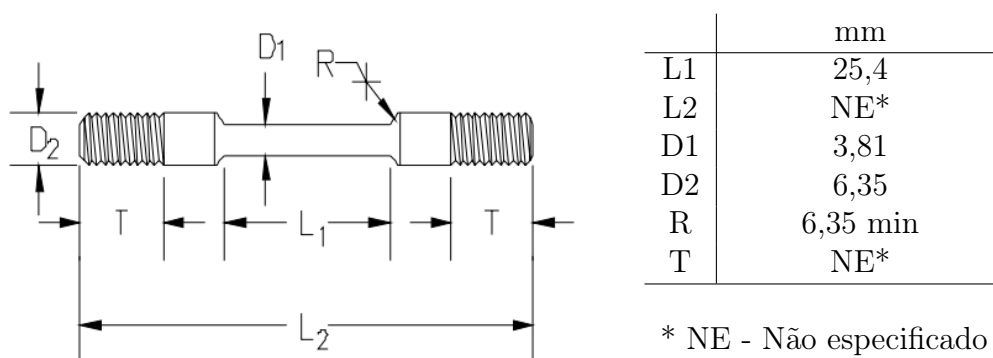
Dimensões do corpo de prova para ensaios mecânicos.
